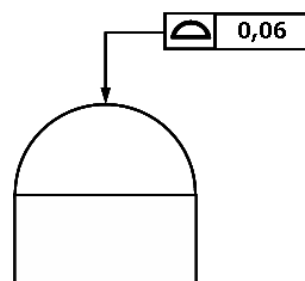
Indicação de tolerância de forma de uma superfície qualquer em desenho técnico
